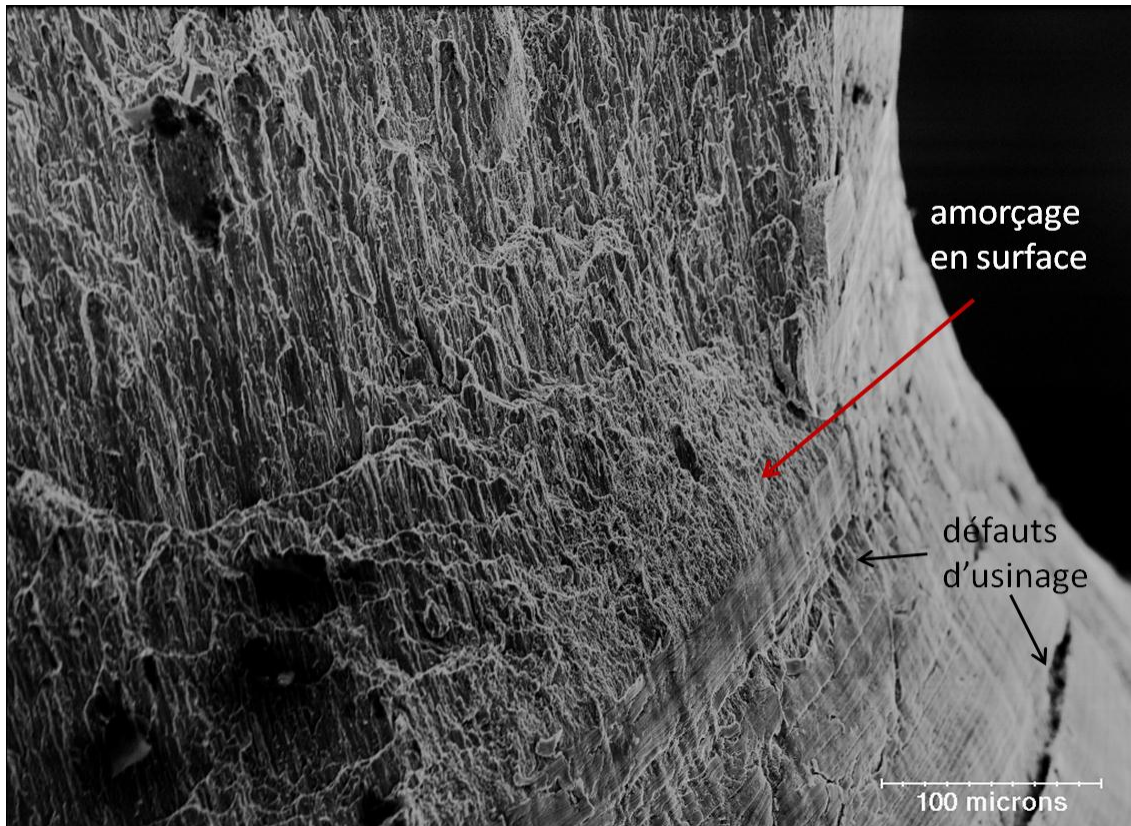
Amorçage de la rupture en surface à partir d'un défaut d'usinage sur une éprouvette de type AE-R2 testée à -120°C.
